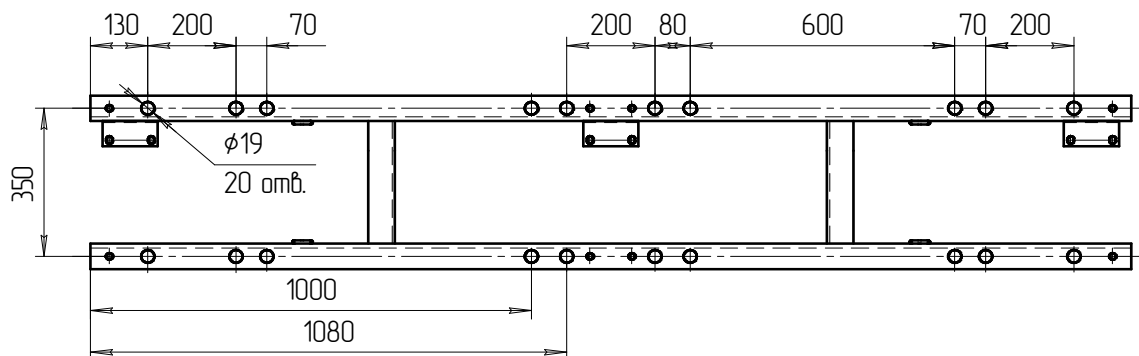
Разметка присоединительных отверстий на общей раме разъединителя
